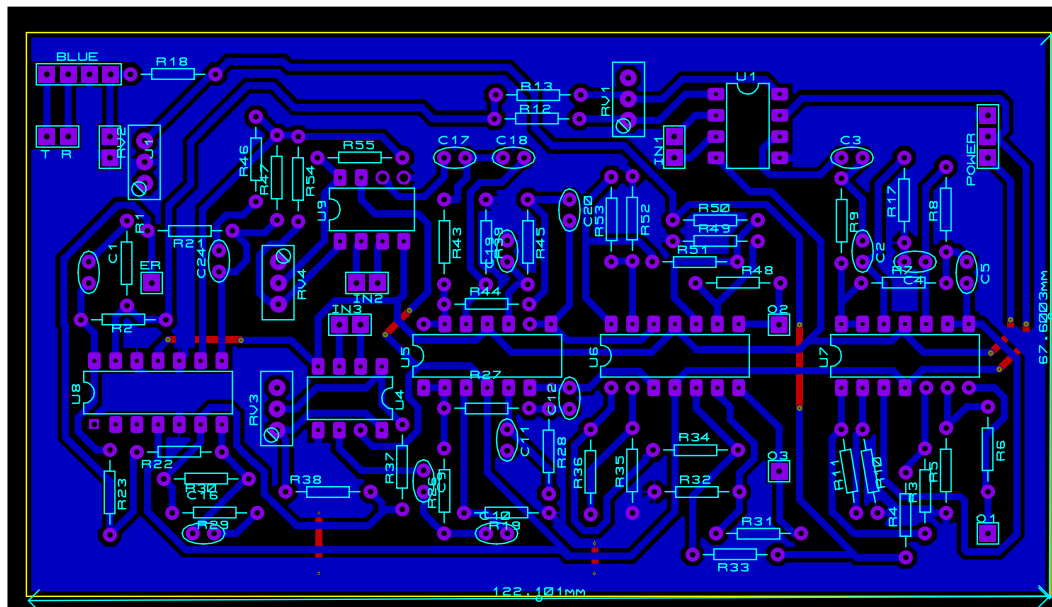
Diseño PCB de la placa acondicionamiento de las señales EMG
